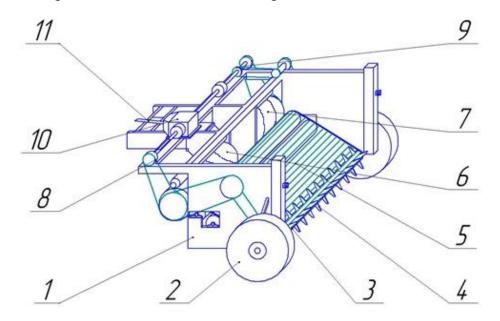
Конструктивно технологическая схема кулачково-планчатого питателя 1 – рама; 2 – опорные колеса; 3 – вал; 4 – кулачки; 5 – цепной транспортер с планками; 6 и 7 – шнеки; 8 и 9 – цепные передачи; 10 – редуктор; 11 – вал
